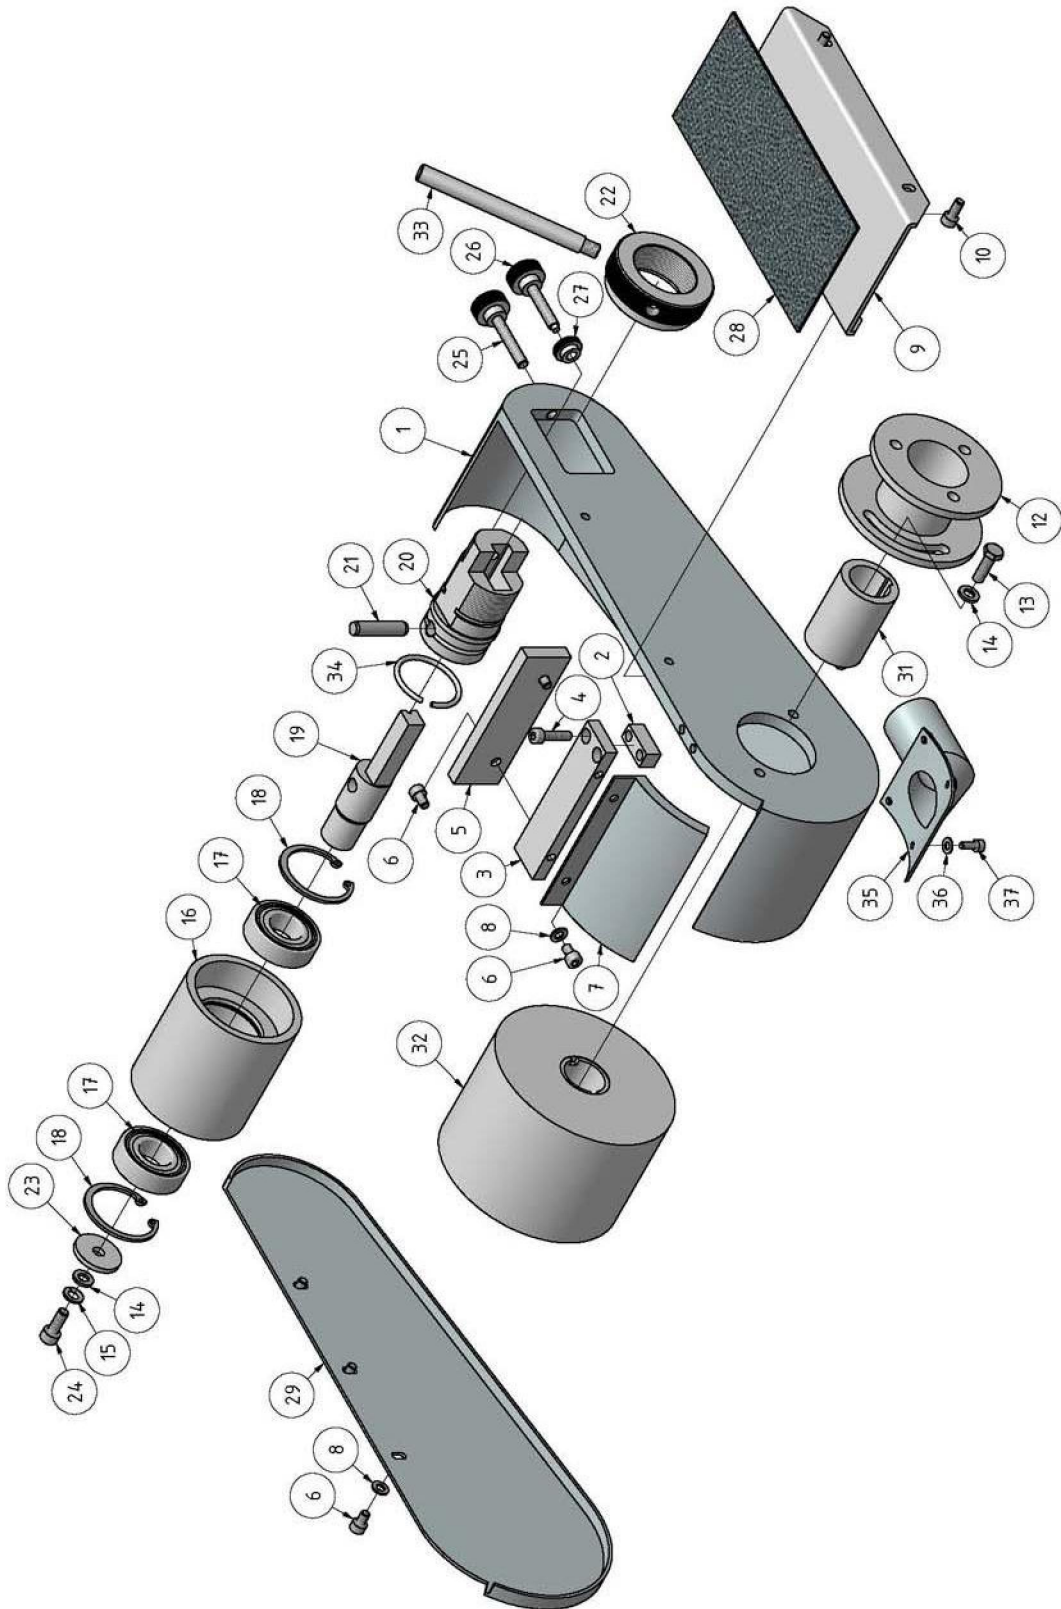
Explosionszeichnung – Esquema piezas de recambio
